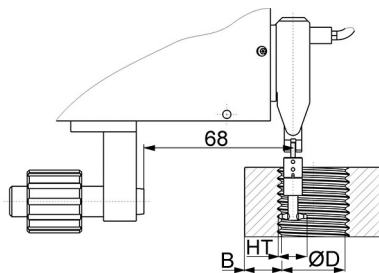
Zubehörbehälter Innengewindemesseinrichtung
